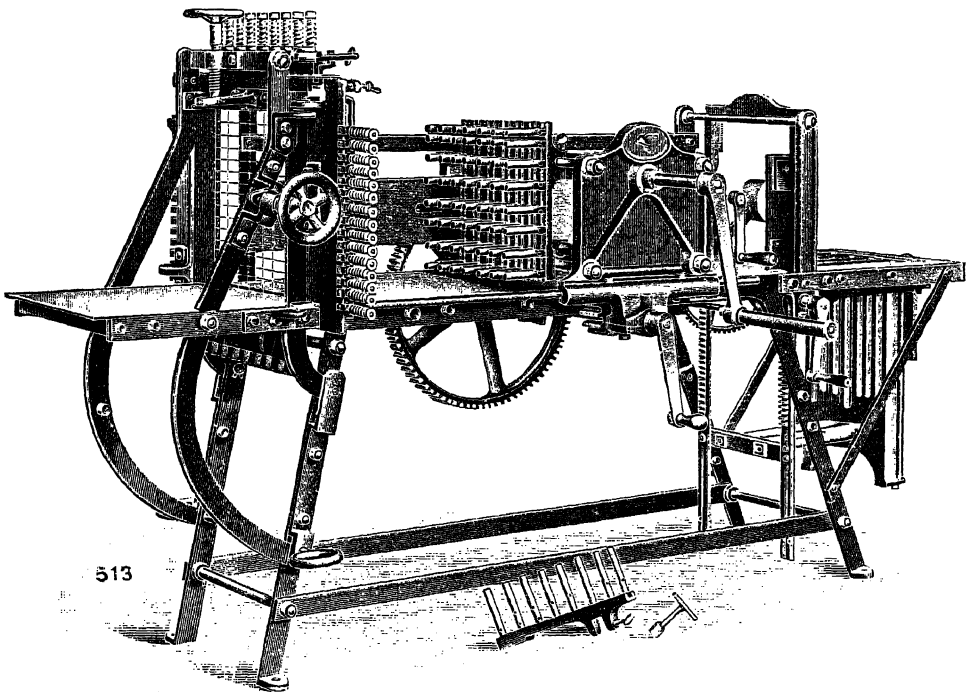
Kombinierte Riegel- und Stückenschnidemaschine.
